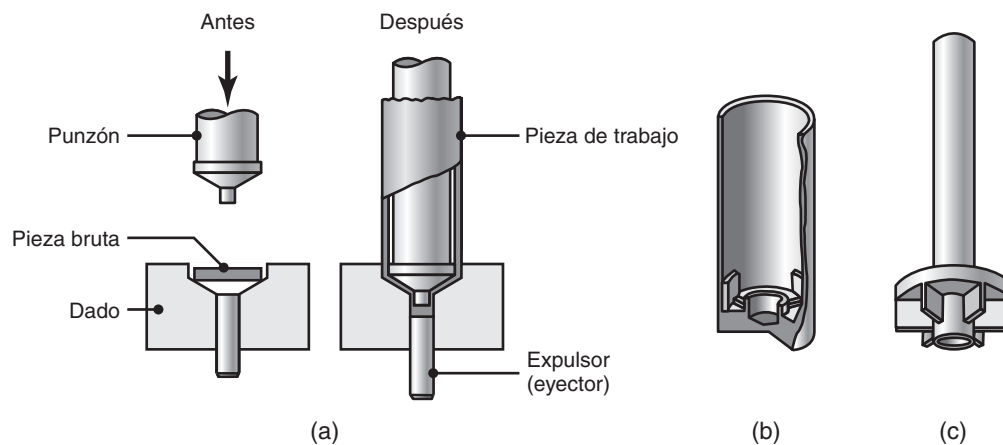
(a) Extrusión por impacto de un tubo plegable mediante el *proceso Hooker*. (b) y (c) Dos ejemplos de productos fabricados mediante extrusión por impacto. Estas partes también se pueden fabricar mediante fundición, forjado o maquinado. La elección del proceso depende de los materiales utilizados, las dimensiones de la parte y el espesor de pared y las propiedades deseadas del producto. Las consideraciones económicas también son importantes en la selección final del proceso.
